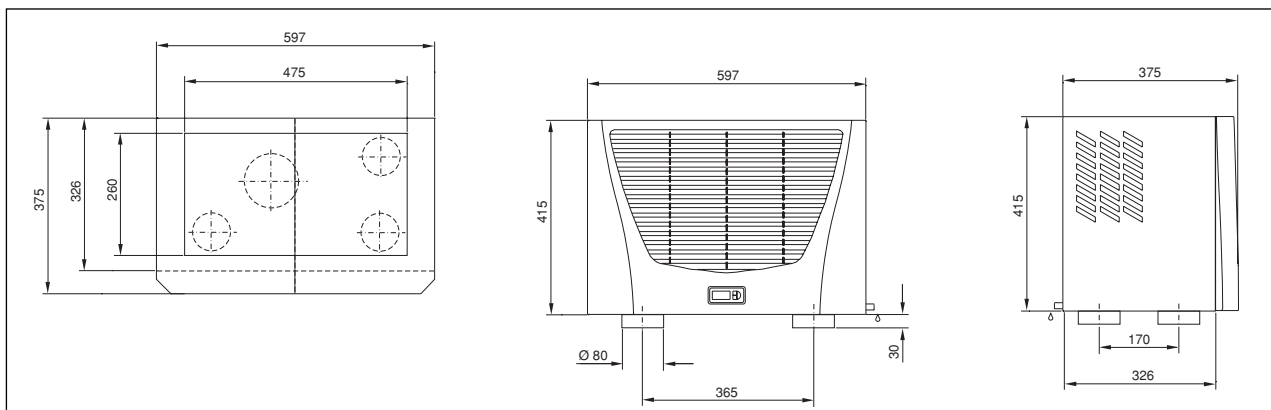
SK 3359.xxx, SK 3382.xxx montage
